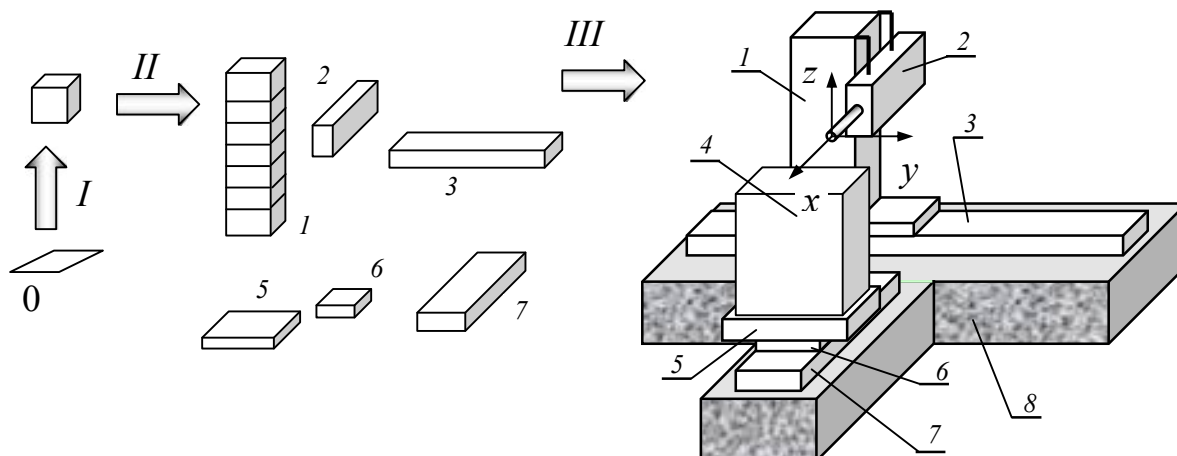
Компоновка тяжелого многоцелевого станка и уровни декомпозиции: 1 – стойка; 2 – шпиндельная бабка; 3 – станина; 4 – обрабатываемая деталь; 5 – паллета; 6 – сани стола; 7 – станина стола; 8 – фундамент
